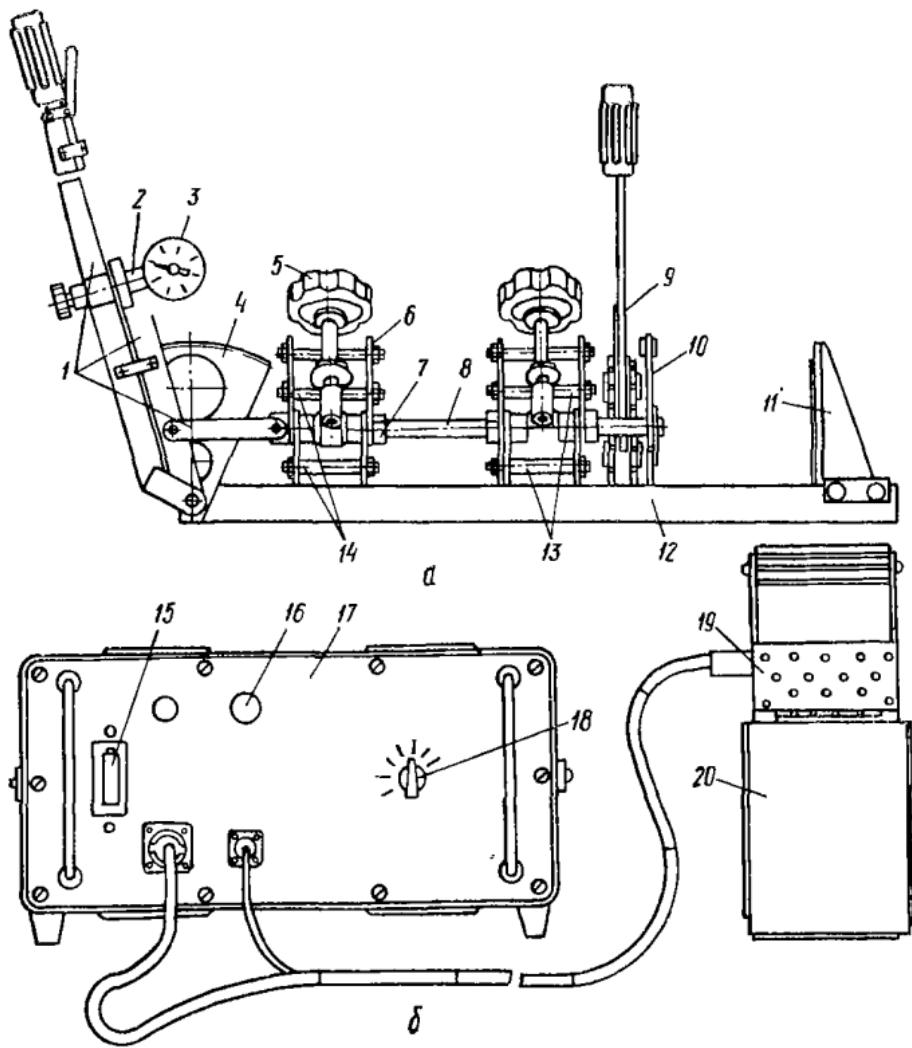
Установка УСТТ-110 для сварки пластмассовых труб:
